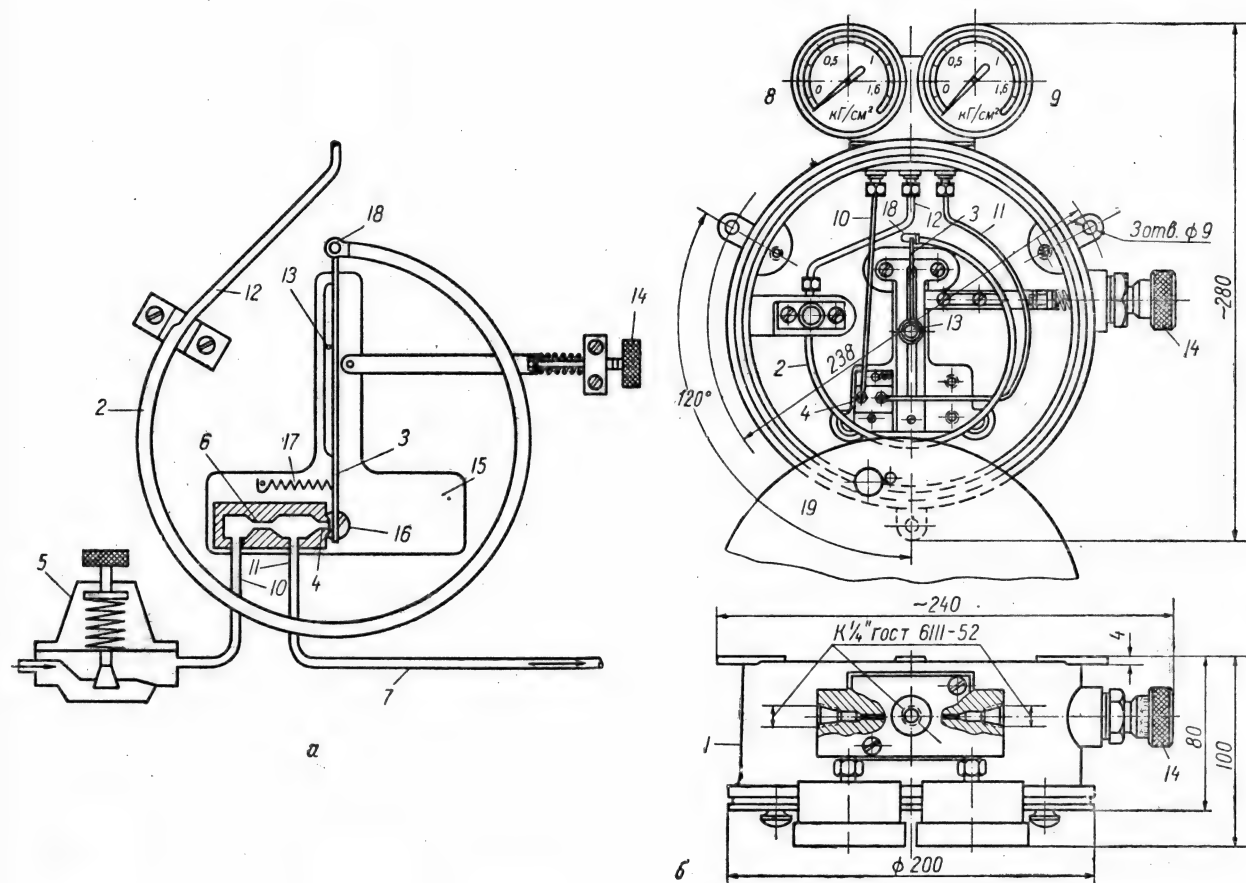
Пневматический регулятор давления типа РД: а — принципиальная схема; б — внешний вид с откинутой крышкой на 180°:
